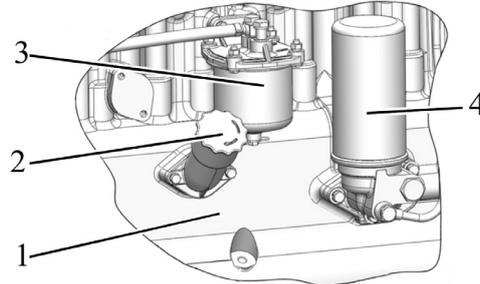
Очистка ротора центробежного масляного фильтра двигателя
